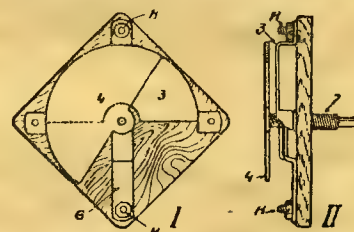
Вид сверху и разрез готового самодельного однопластинчатого конденсатора.
